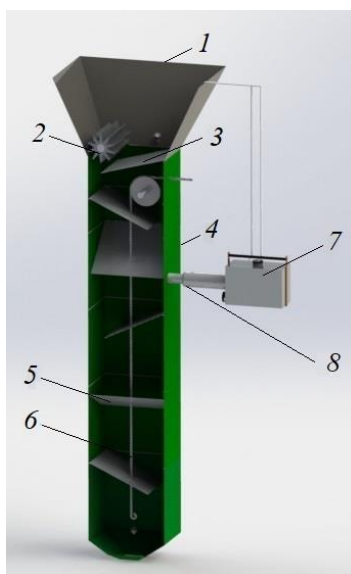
Схема пристрою для обробки насіння гарячим туманом: 1 – бункер для насіння; 2 – дозувальний апарат із приводним ребристим валиком; 3 – рухоме днище; 4 – камера обробки; 5 – похилі полиці; 6 – тросово-барабанний механізм; 7 – аерозольний генератор; 8 – сопло.
